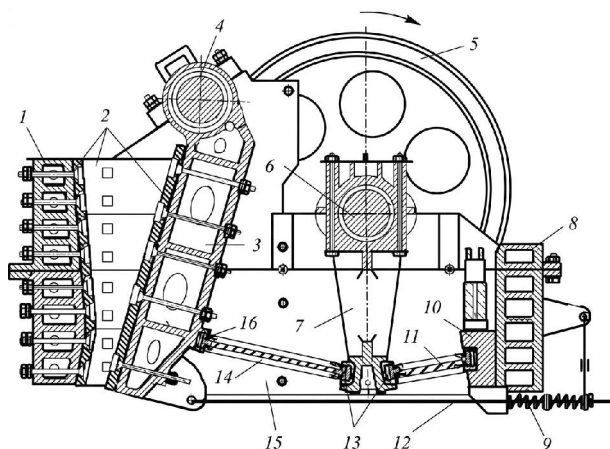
Кінематична схема щоккової дробарки з простим рухом щоки типу ЩДП:
